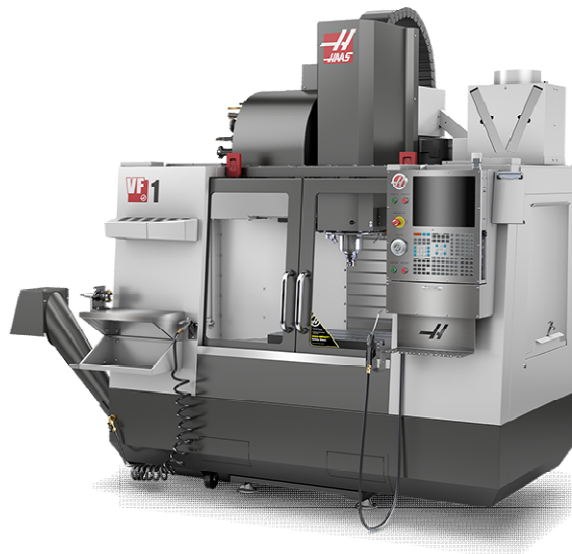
Вертикально–фрезерний верстат з ЧПК Haas VF–1
